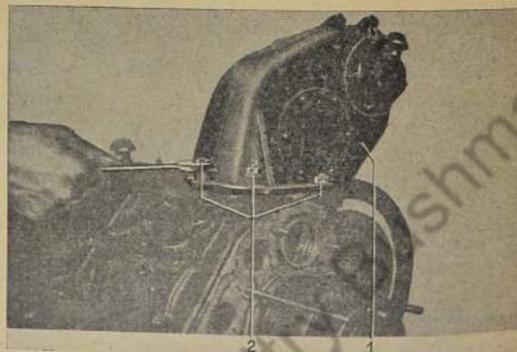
Zwischenradgehäuse aufsetzen und verschrauben
